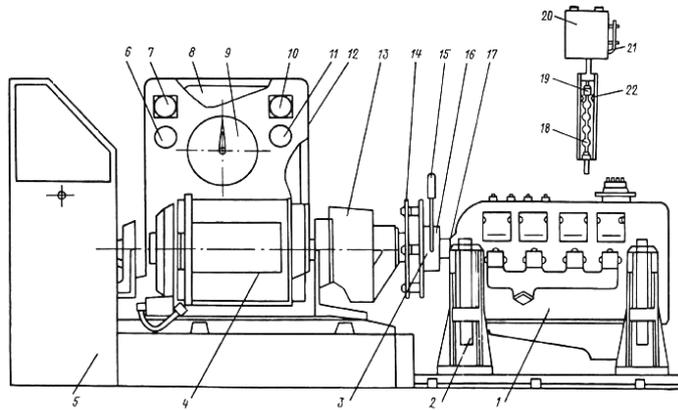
Стенд для обкатки и испытания двигателя внутреннего сгорания (КИ-5543):
